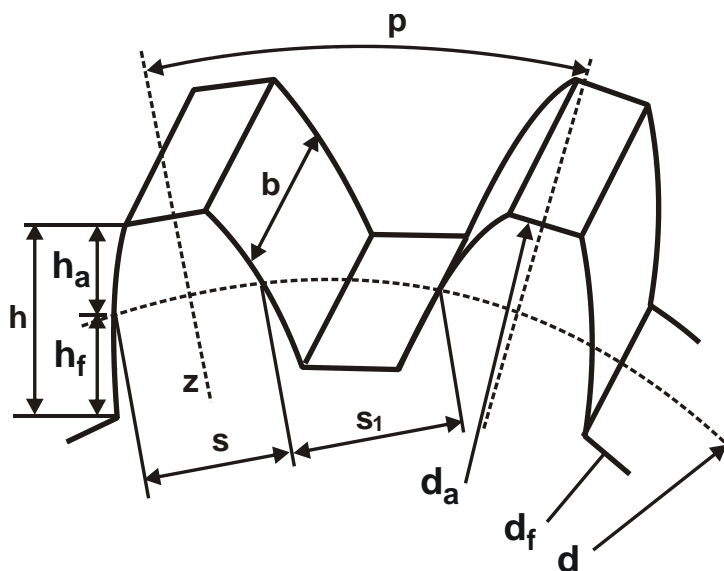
Геометричні параметри зуба зубчастого колеса
